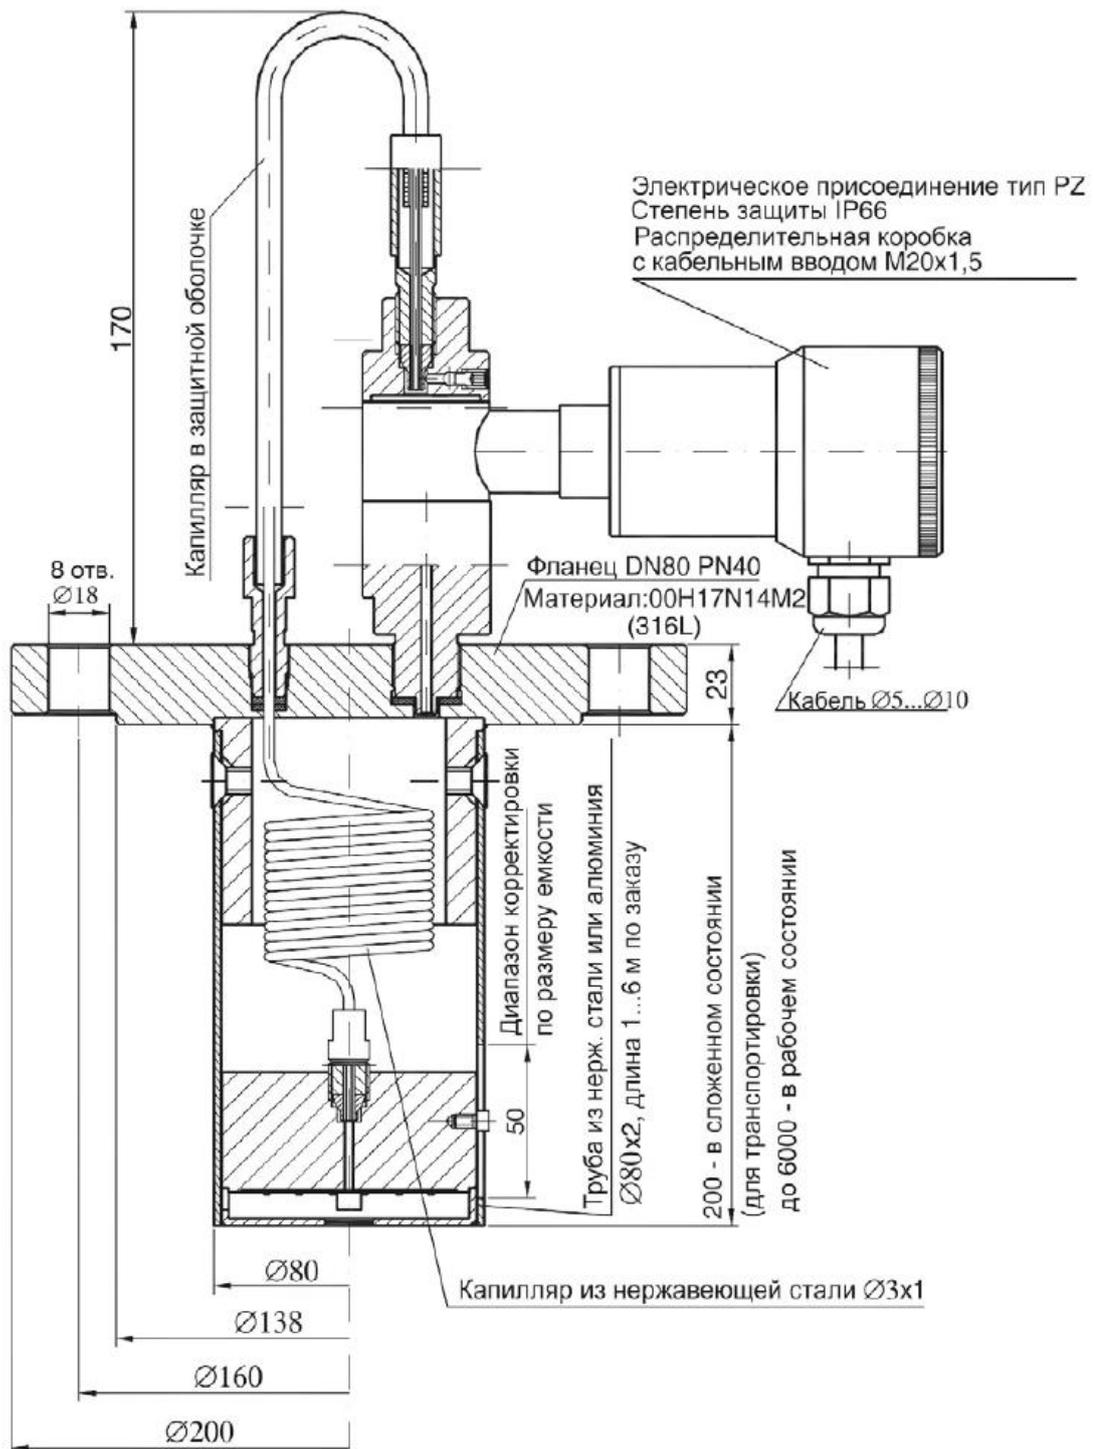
Внешний вид, установочные и соединительные размеры преобразователей APR-2200
